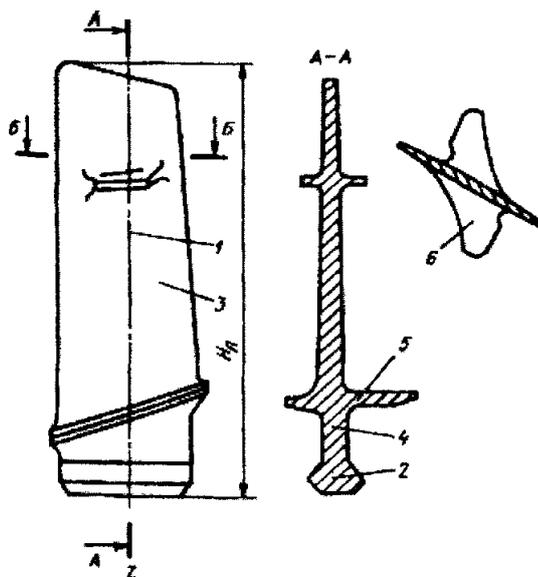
Рабочая лопатка ротора компрессора: 1 - ось лопатки; 2 - хвостовик; 3- перо; 4 - ножка хвостовика; 5 - полка хвостовика; 6 — антивибрационная полка; лл - длина лопатки
